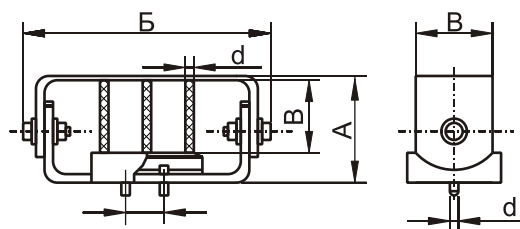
Шинодержатели ШР-5-375, ШР-6-375, ШР-11-750, ШР-12-750, ШР-12-2000
